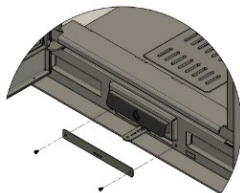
Retire los tornillos; coloque la pieza de sellado y vuelva a apretar los tornillos.
